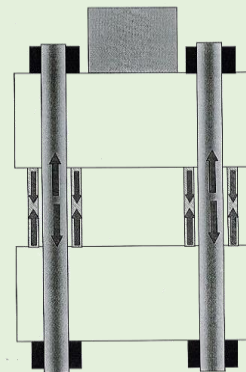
Estructura en columnas de prensas hidráulicas de medio tonelaje. Imagen: SACMI.
